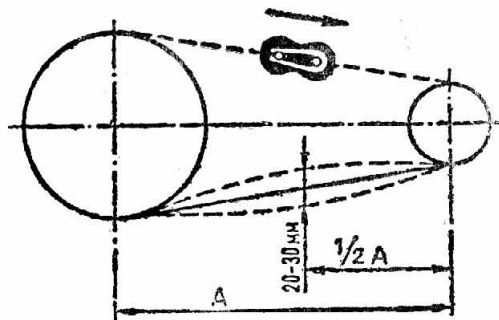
Установка защелки замка цепи, контроль натяжения цепи
